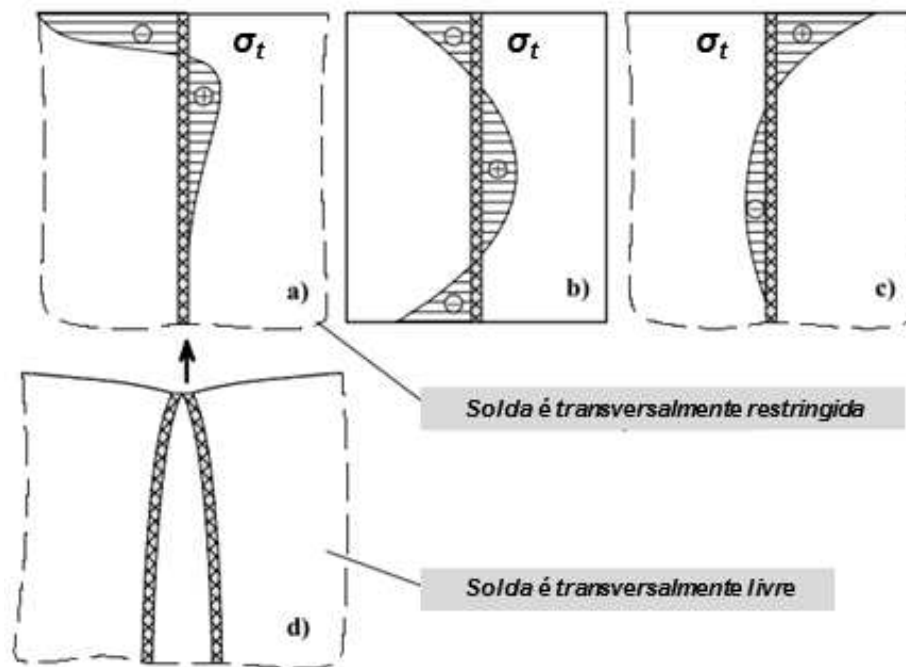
Tensões residuais transversais devido à soldagem com único passe em: (a) solda depositada rapidamente em placas longas, (b) solda rapidamente depositada em placas curtas, (c) solda lentamente depositada em placas longas e (d) configuração final de uma junta soldada sem restrições transversais. Adaptado de Pilipenko (2002).
